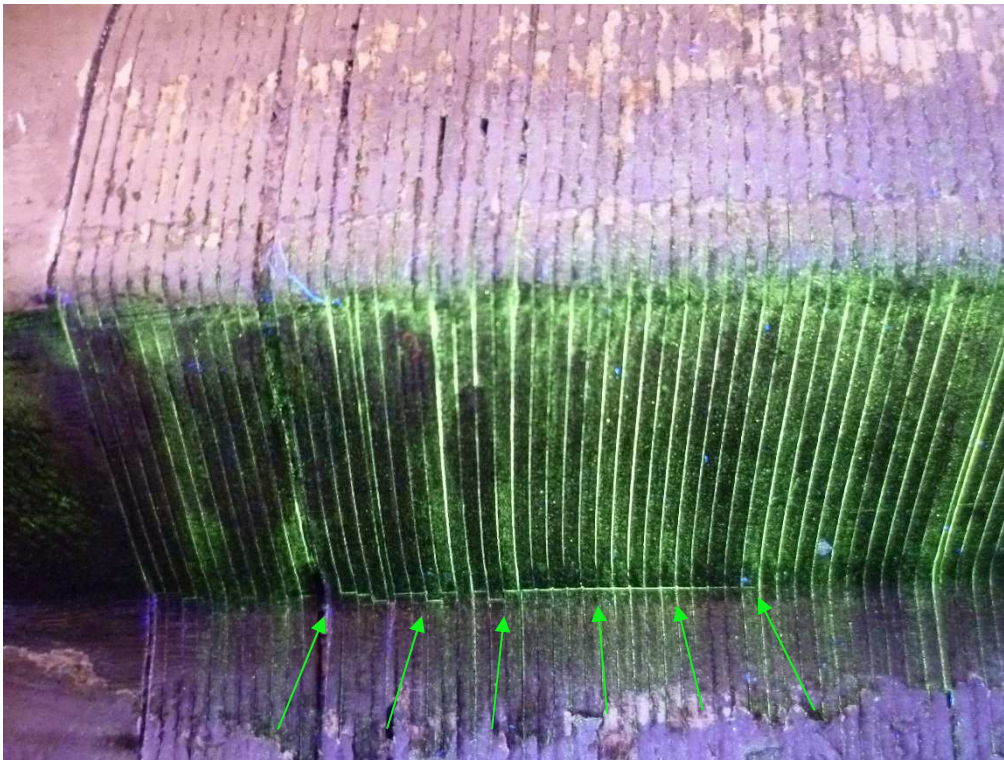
Beispiel einer MT Anzeige in einer Hammerkopfnut.
